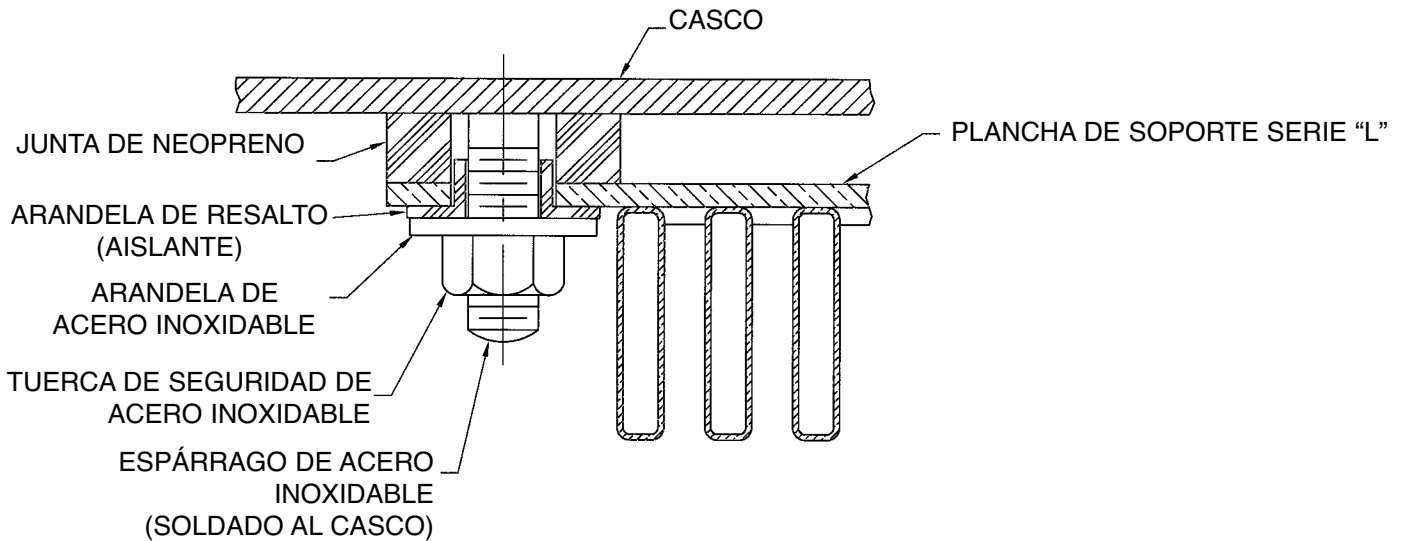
Plancha de soporte SERIE L con el espárrago soldado al casco
